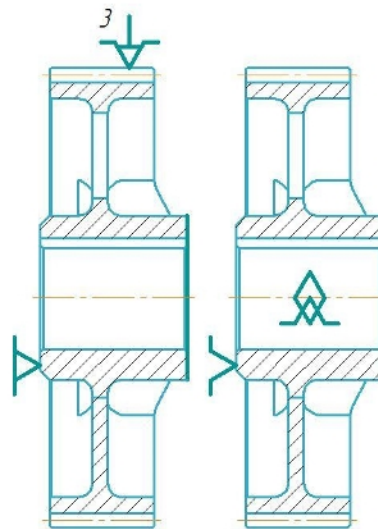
Умовна та теоретична схема базування зубчастого колеса
